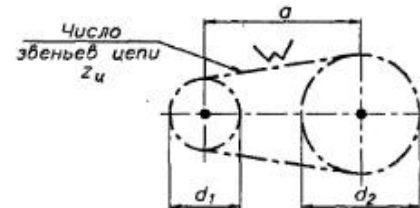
Схема и основные размеры передачи с приводной зубчатой цепью
